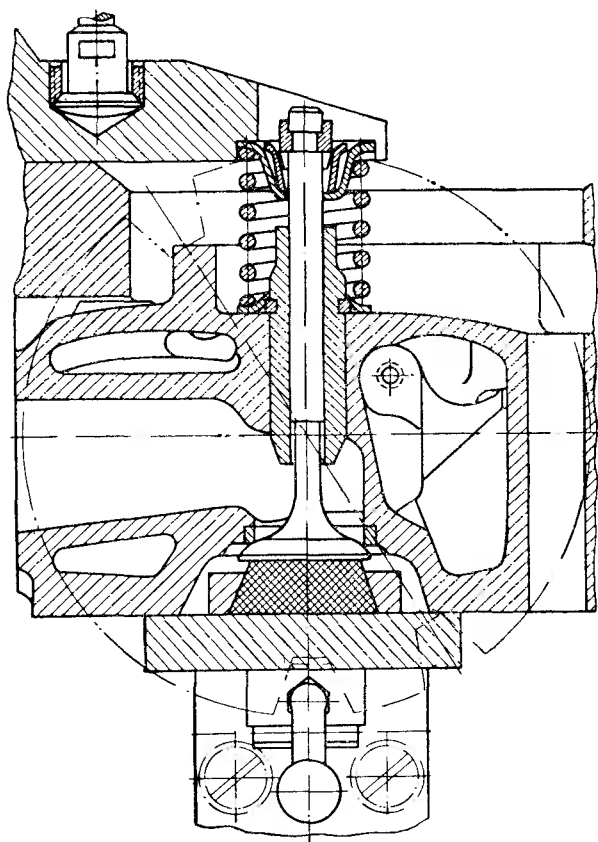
Сжатие клапанных пружин пневматическим зажимом и установка сухариков клапана
